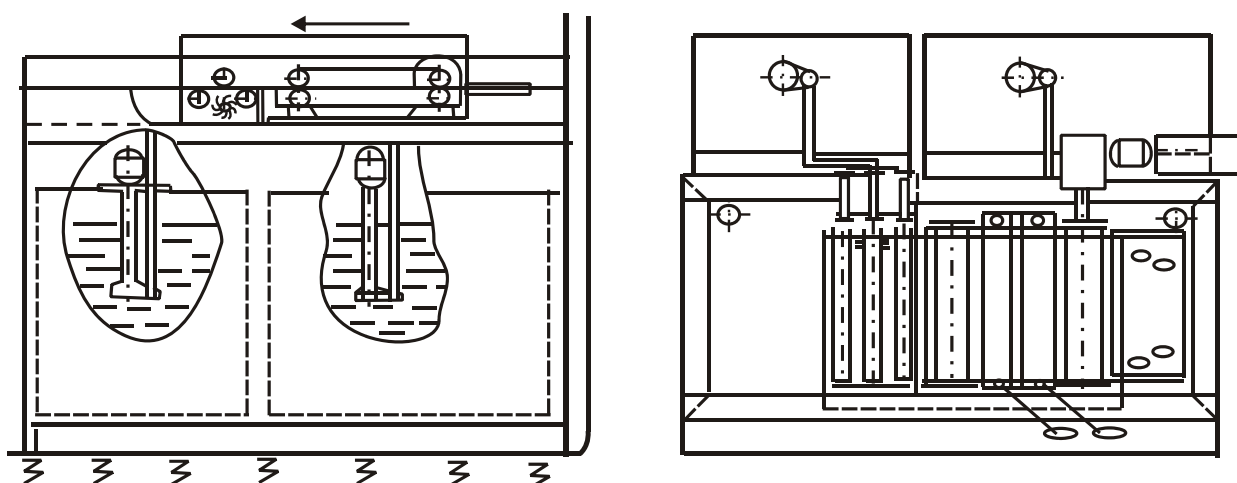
Загальний вигляд пристрою для електрохімічної обробки плоских деталей із листових матеріалів
